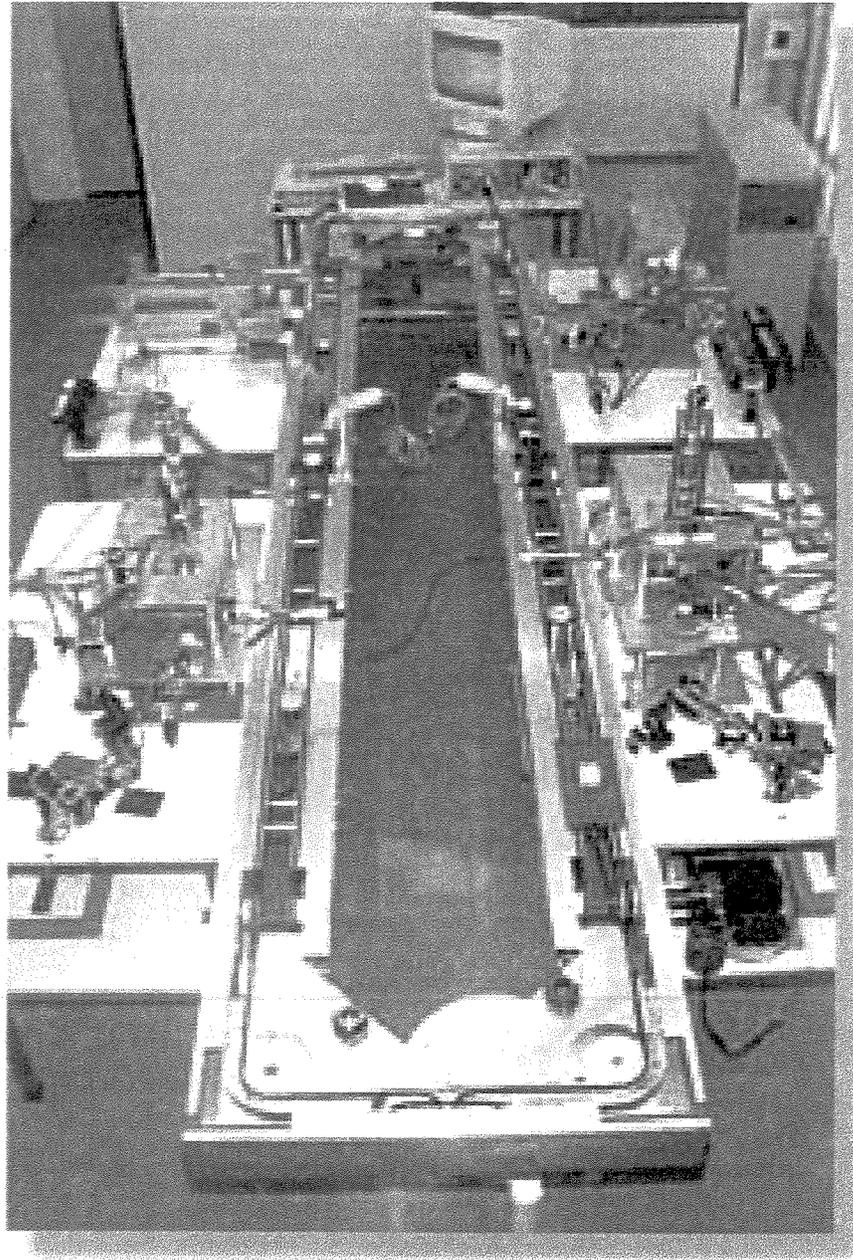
Vista geral da Plataforma PIPEFA (Fonte – LAIR UNICAMP).
